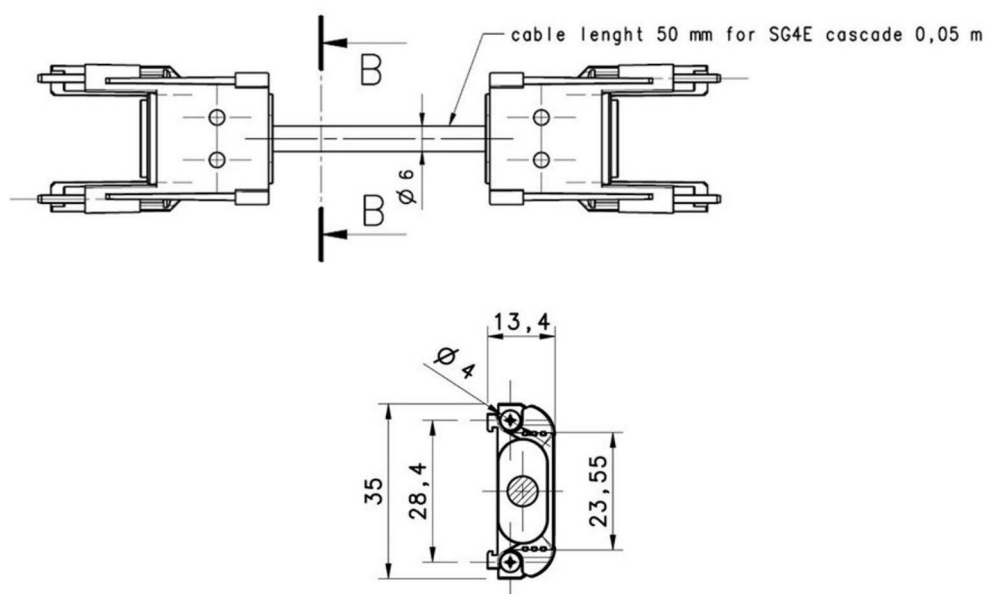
Dimensiones CS-F1-80-B-0005 (mm)
